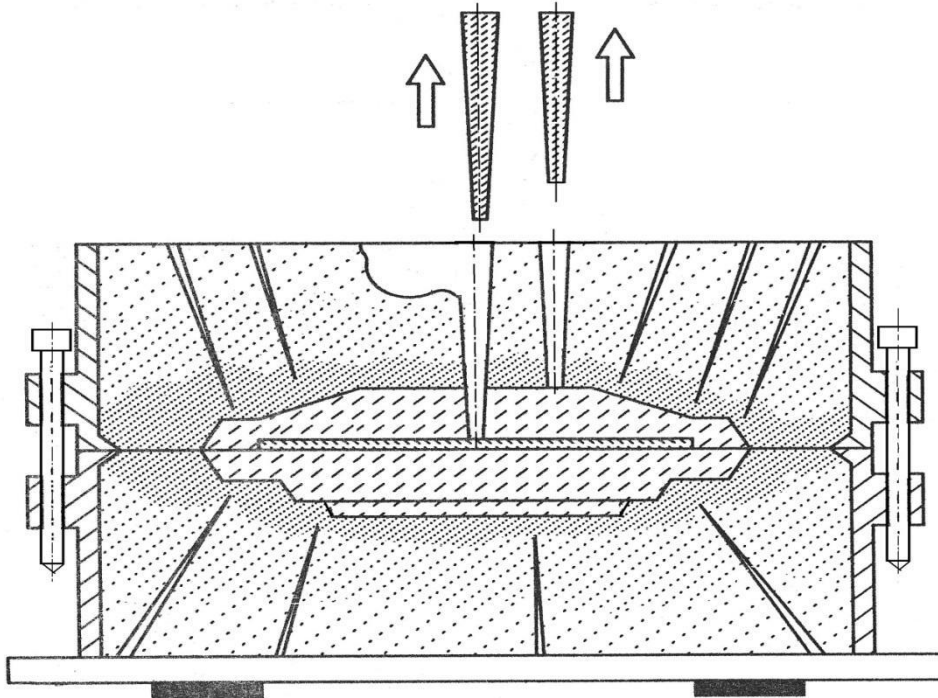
Zaformovaný model s vtokovou soustavou v dělené formě
